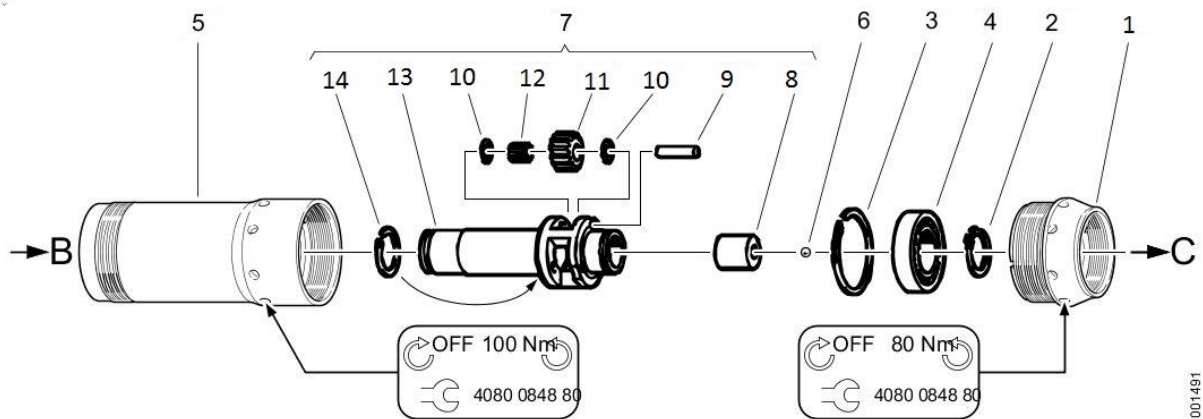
Imagem mostra conjunto de engrenagem da apertadeira
